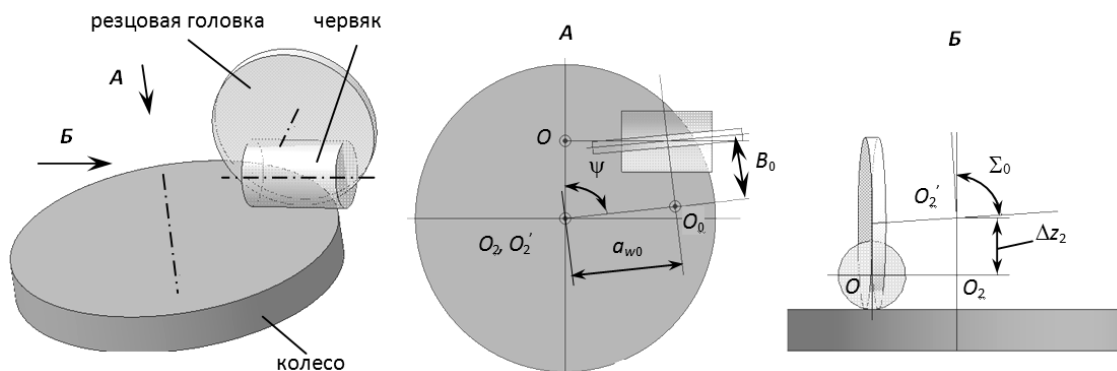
Воображаемое общее зацепление червяка, колеса и резцовой головки
